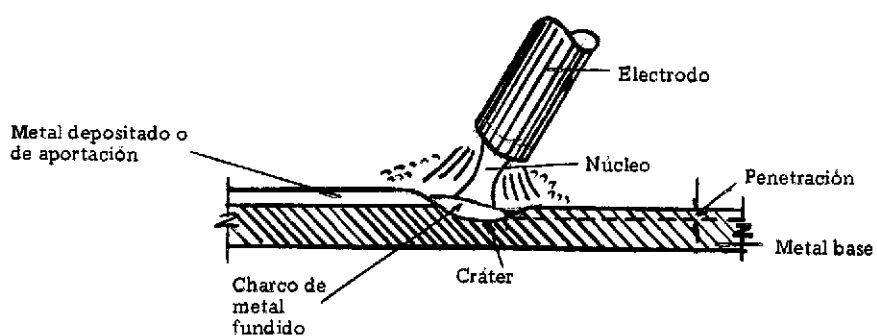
Soldadura de arco sin protección.
